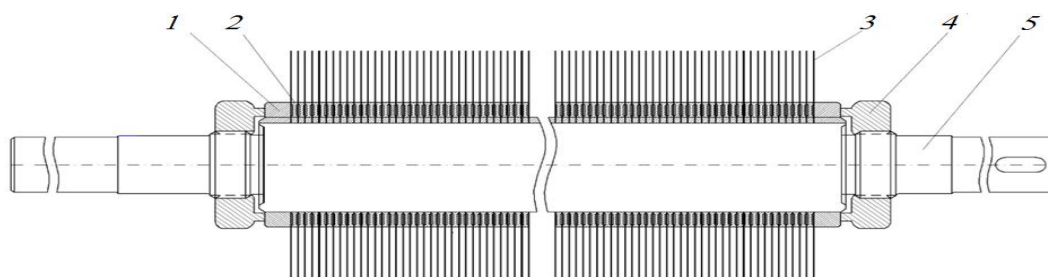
Пильный цилиндр пильного джина марки 4ДП-130
